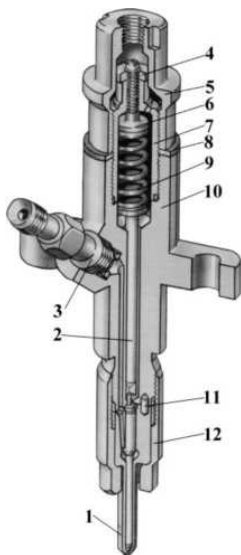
Устройство форсунки: 1 - распылитель; 2 - штанга; 3 - штуцер подвода топлива; 4- контргайка; 5 -колпак форсунки; 6 - регулировочный винт; 7 - гайка пружины; 8 - прокладка; 9 - пружина; 10 - корпус форсунки; 11 -штифты; 12 - гайка распылителя.
